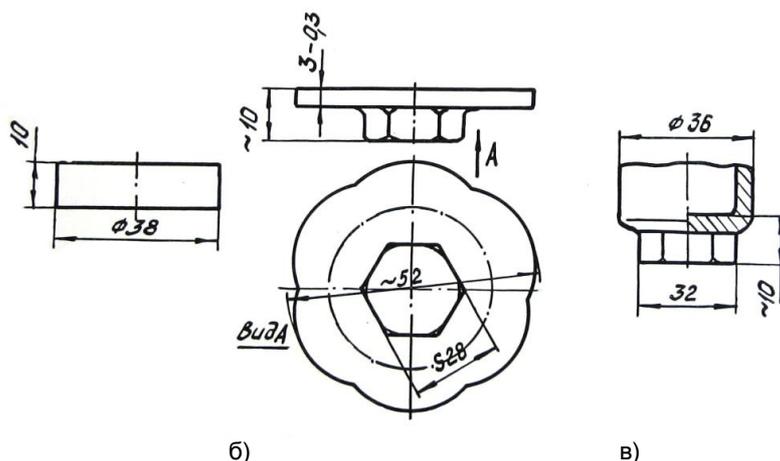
Технология холодной объемной штамповки крышки гидросистемы: а – исходная заготовка; б – контурная осадка заготовки на матрице с шестигранным отверстием; в – операция вытяжки-свертки
